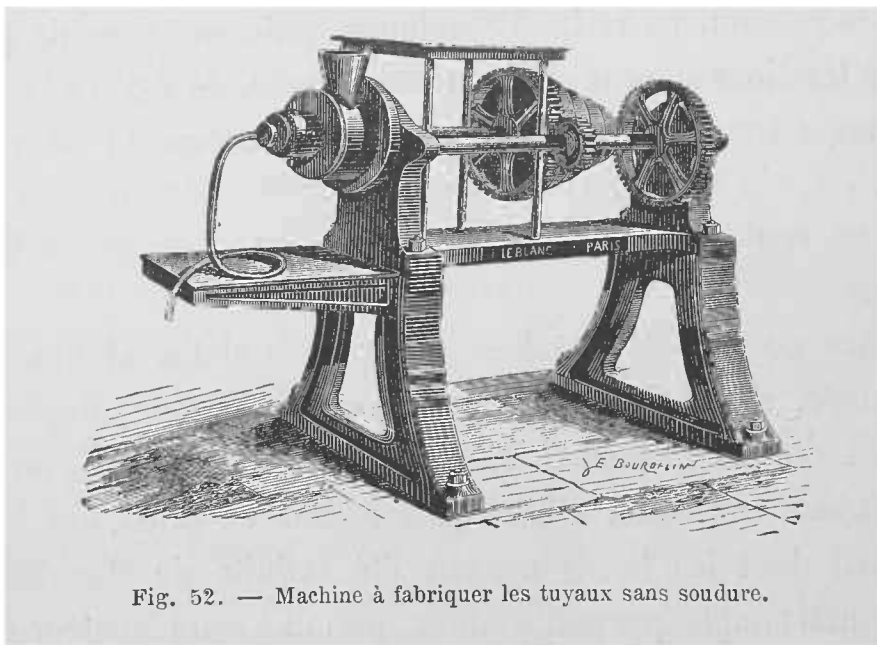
Machine à fabriquer les tuyaux sans soudure.
